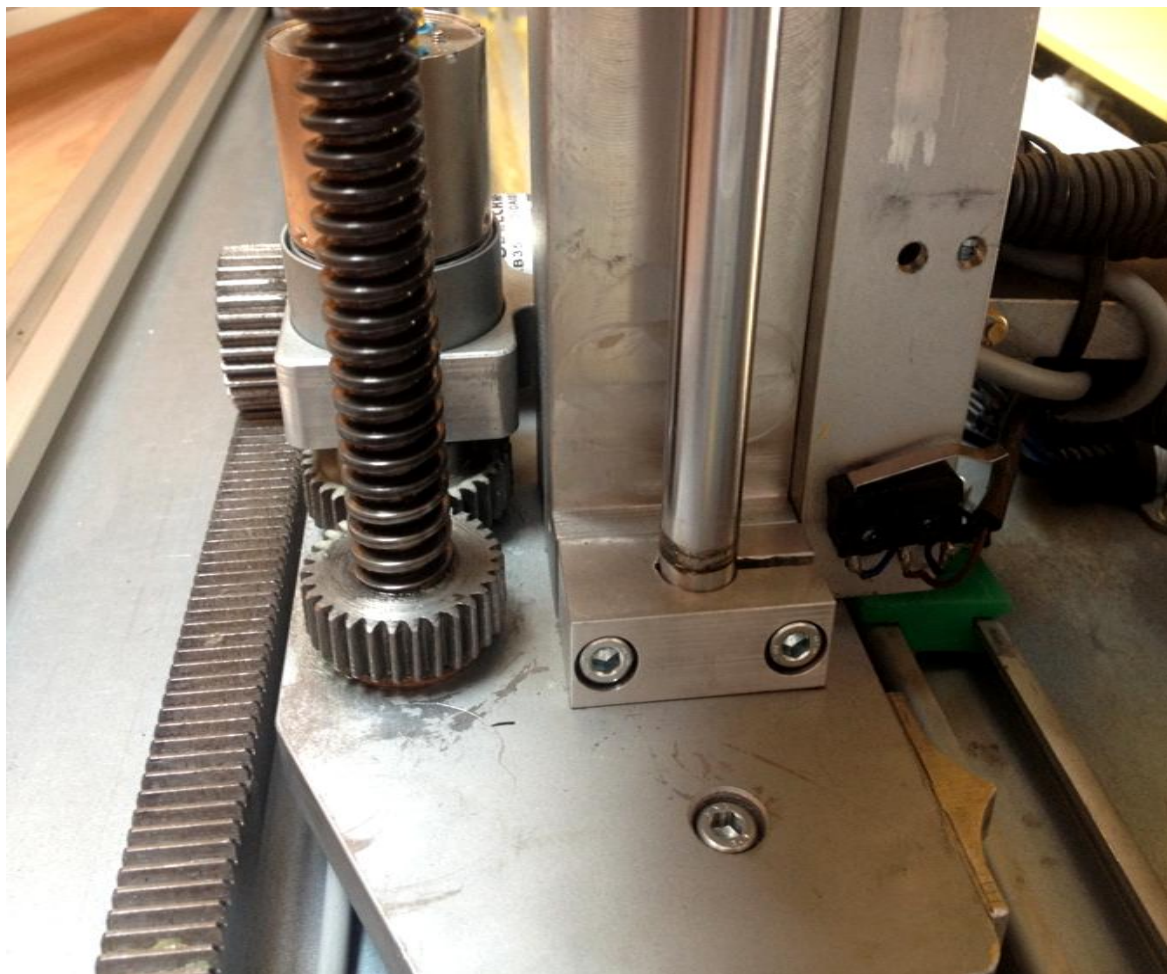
Původní řešení pohybu zakladače palet v ose y
